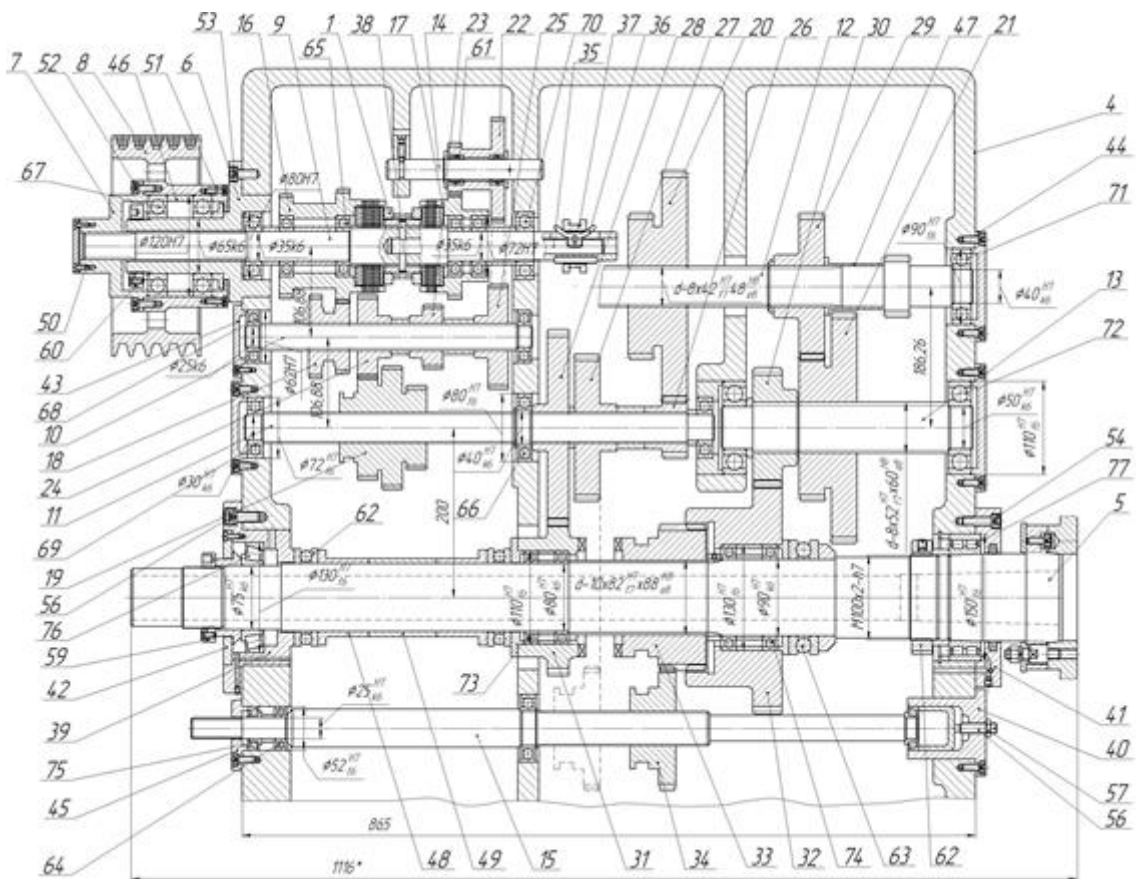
Поздовжня компоновка коробки швидкостей токарно-гвинторізного верстату 1А62
